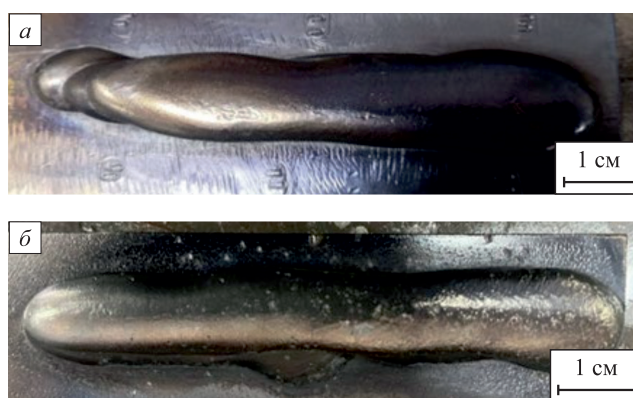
Характерный вид наплавленных образцов: а – образец К3; б – образец К4
